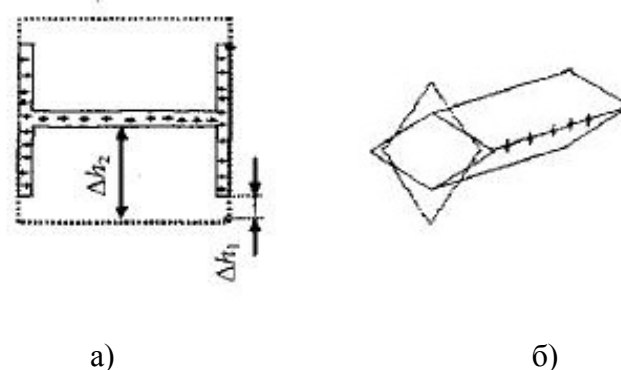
Прокатка двутавра (а), прокатка ромбической заготовки (б)
